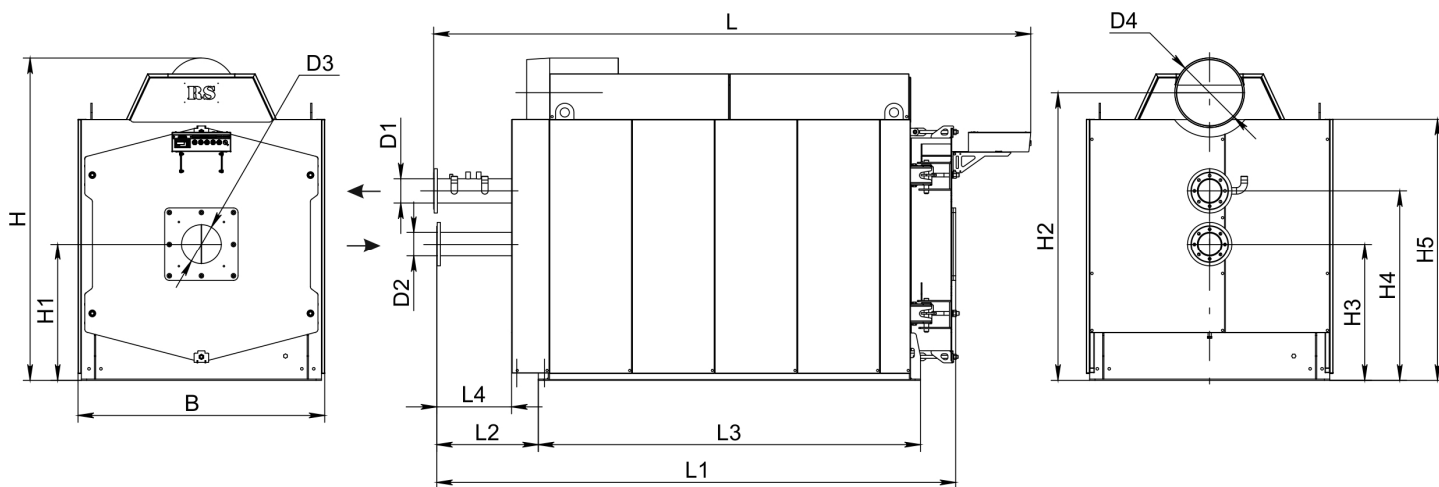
Габаритные и присоединительные размеры котлов RS-D1500 - RS-D2500
